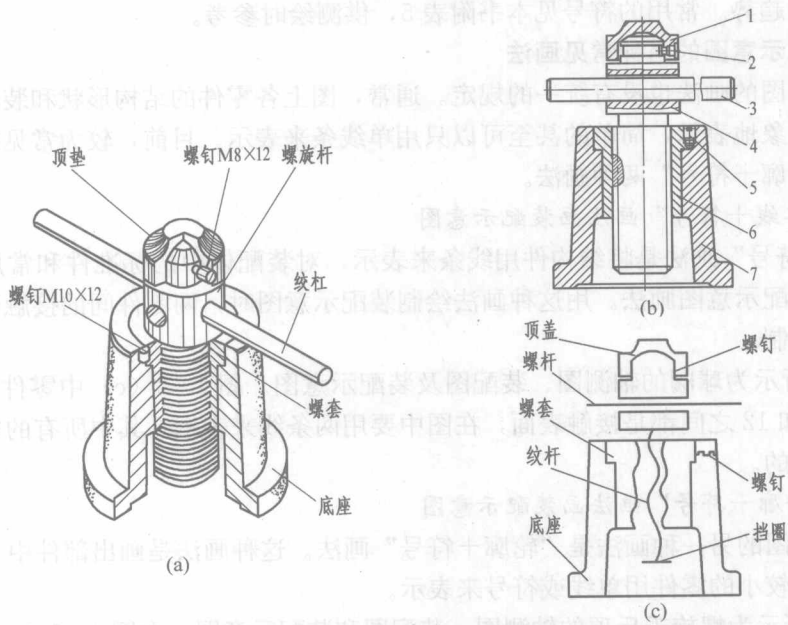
螺旋千斤顶的轴测图、装配图和装配示意图
